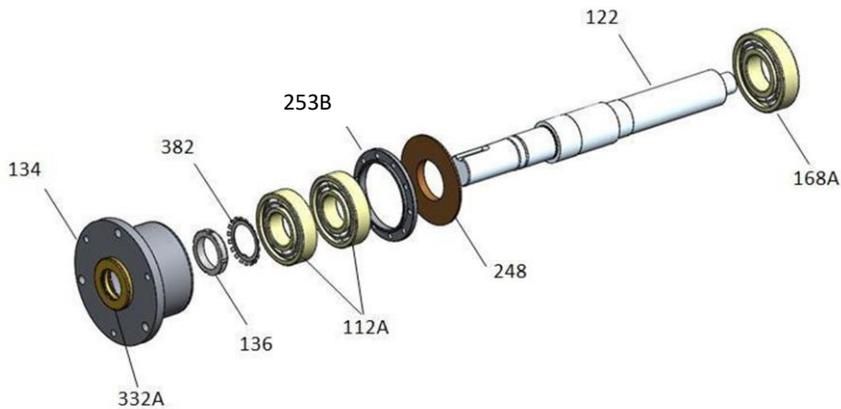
Extracción del rodamiento - Grupo 1 y 2 de rodamientos dobles
